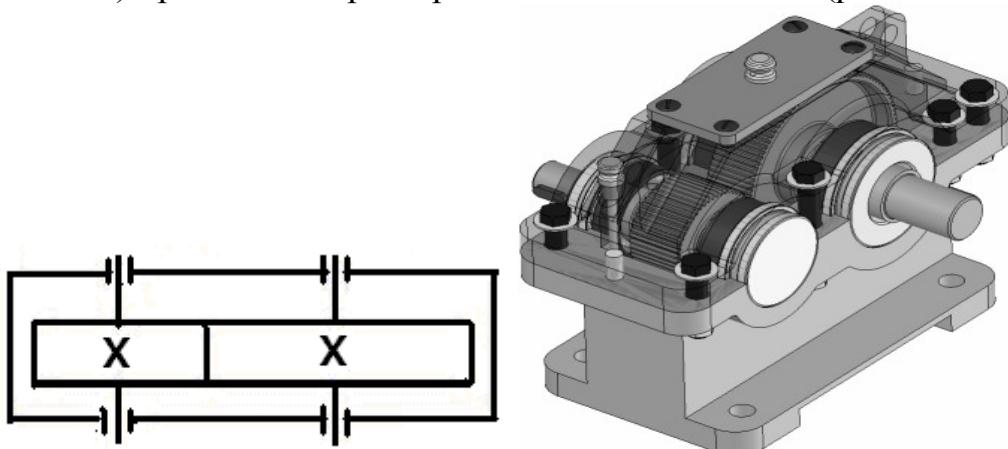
Цилиндрический одноступенчатый редуктор
